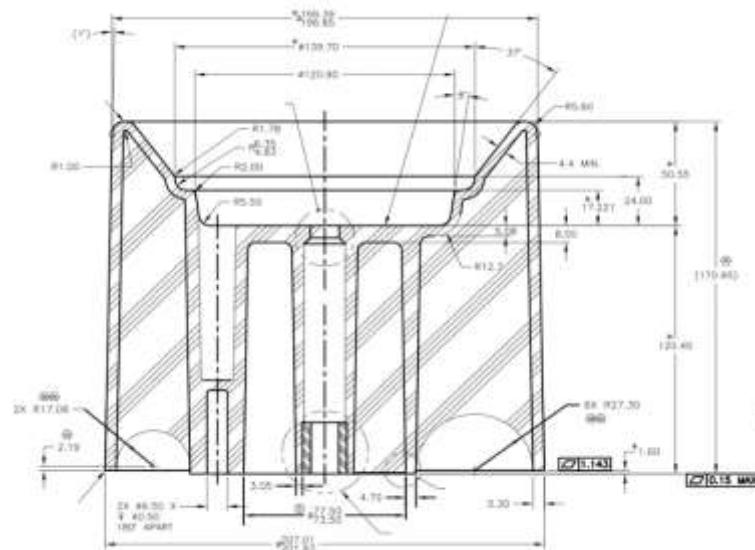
Desenho técnico do pistão, vista lateral, corte até o centro, com dimensões em milímetros. Fonte: Firestone IP.
